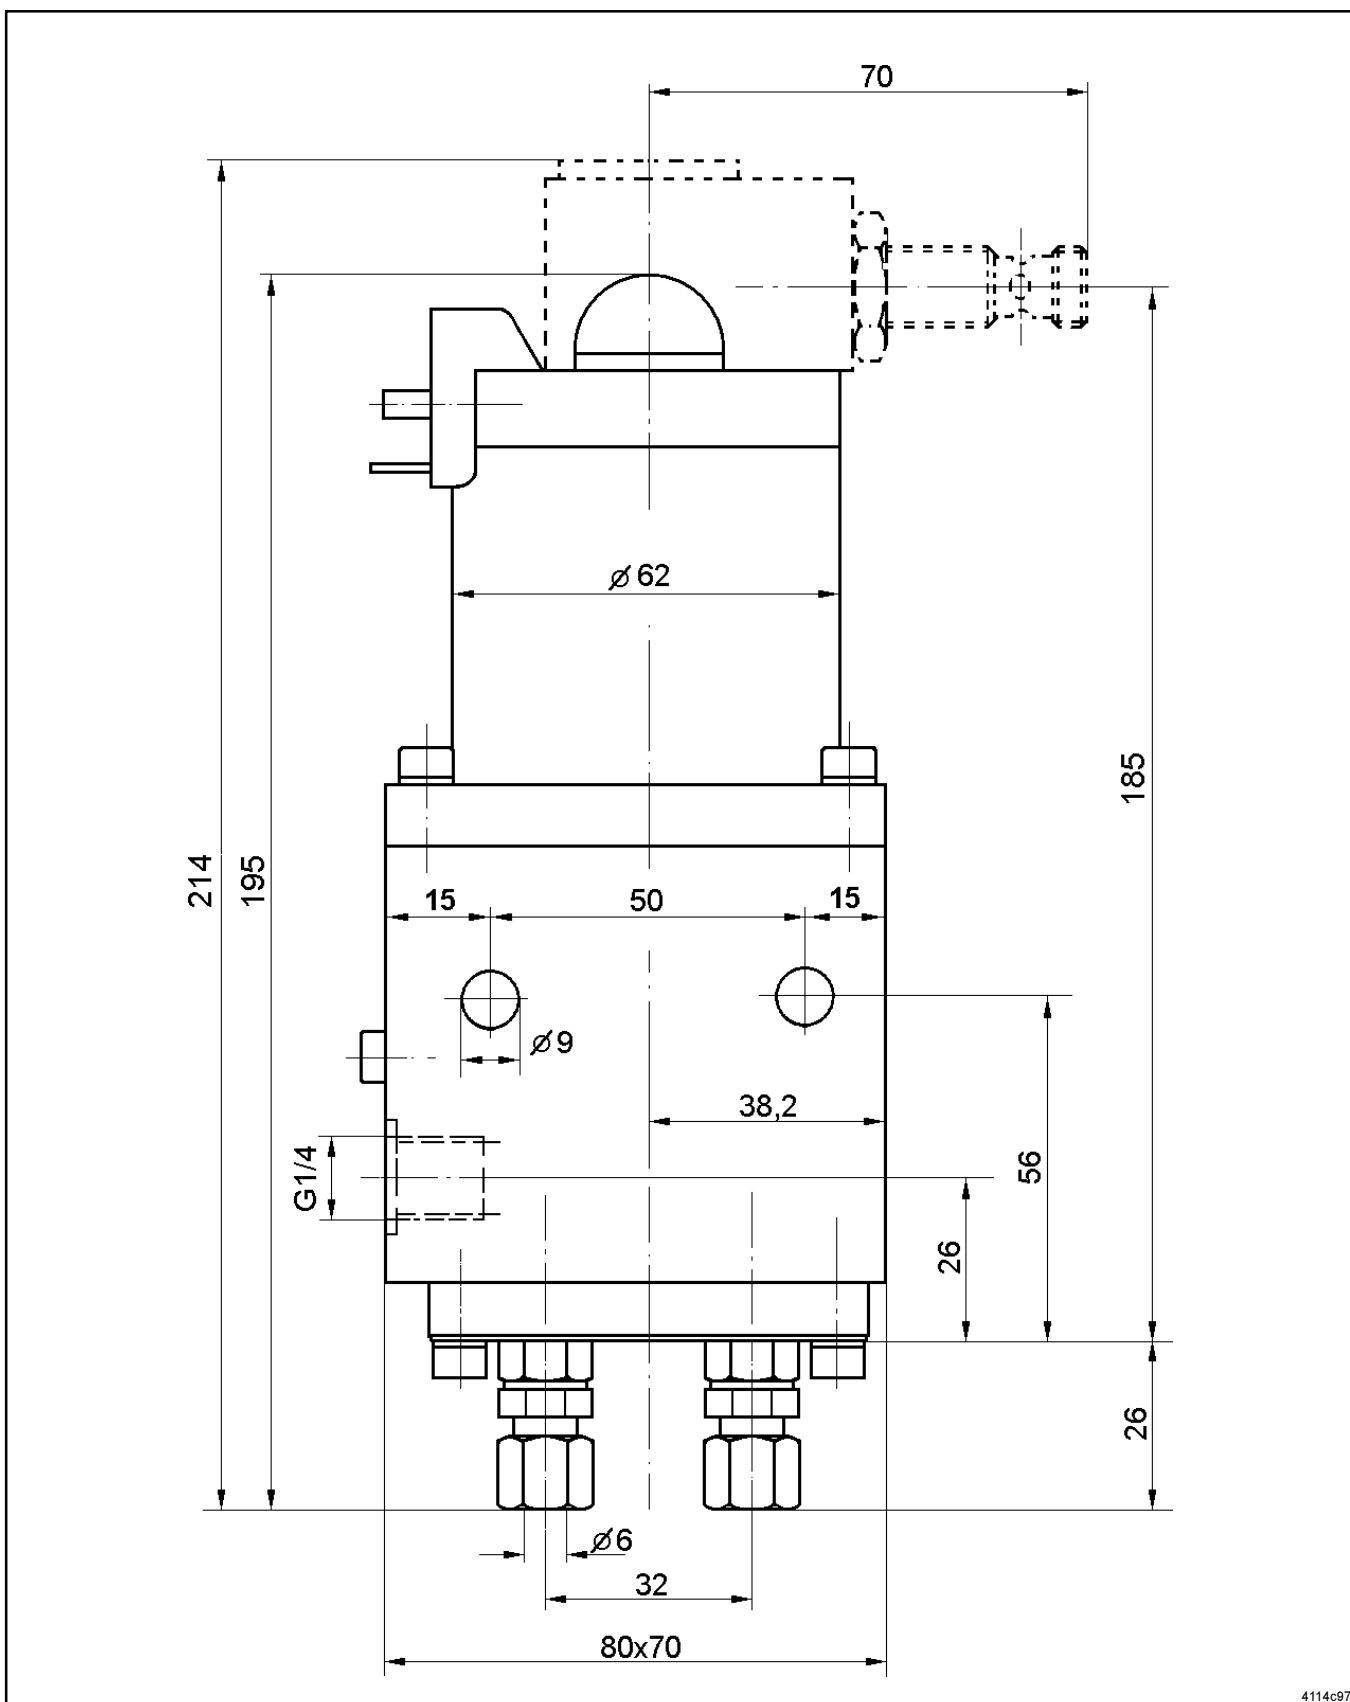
Abmessungen der Pumpe PMA - 1 (KN) ohne Magnetstecker
